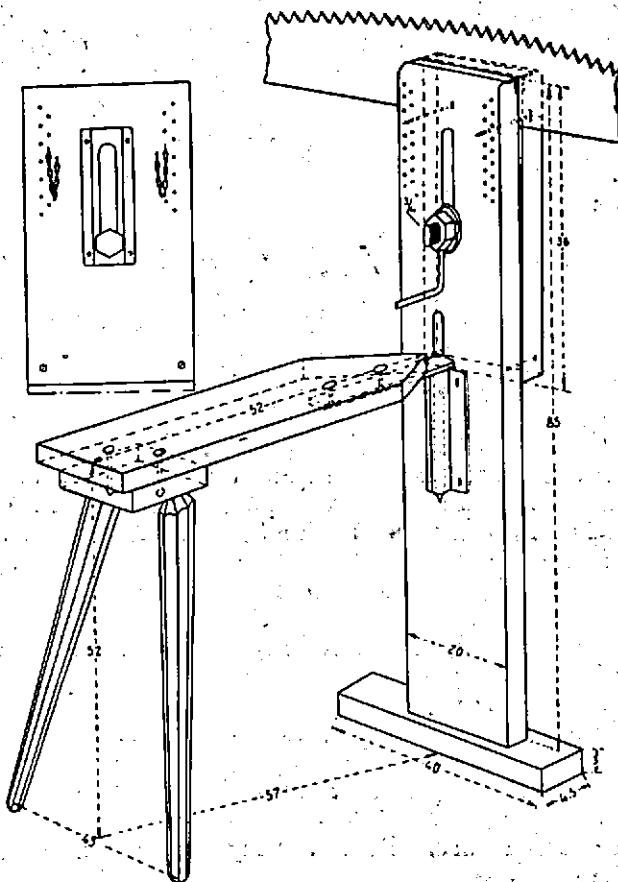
Bok voor de behandeling van zagen, systeem, Burki.
